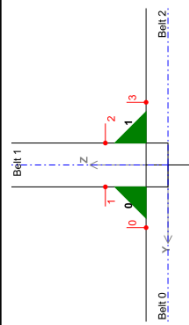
Schweißnahtdetail B_VC
